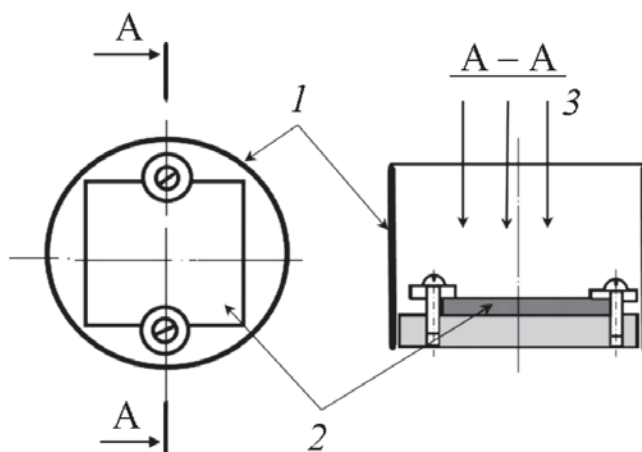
Приспособление для облучения образцов из алюминиевого сплава в установке ПФ «Вихрь»: 1 — цилиндрический экран из медной фольги толщиной 0,2 мм, 2 — образец, 3 — поток ионов гелия и гелиевой плазмы.
